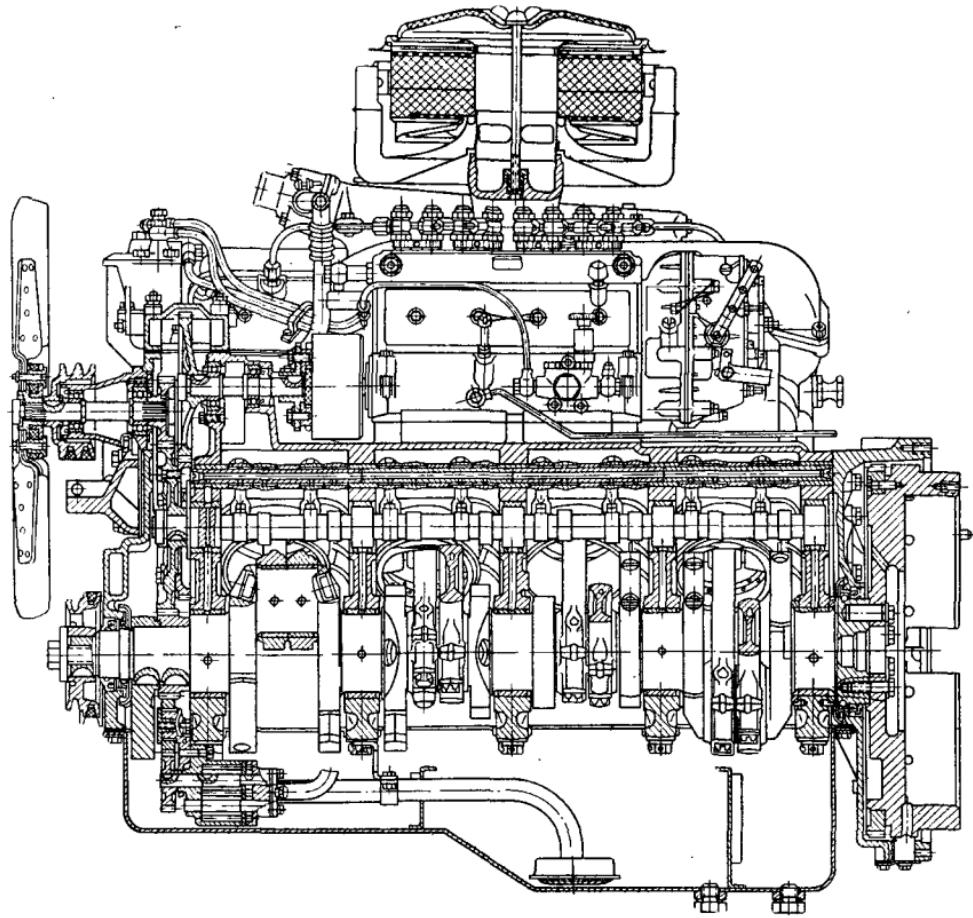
Продольный разрез двигателя ЯМЗ-238
